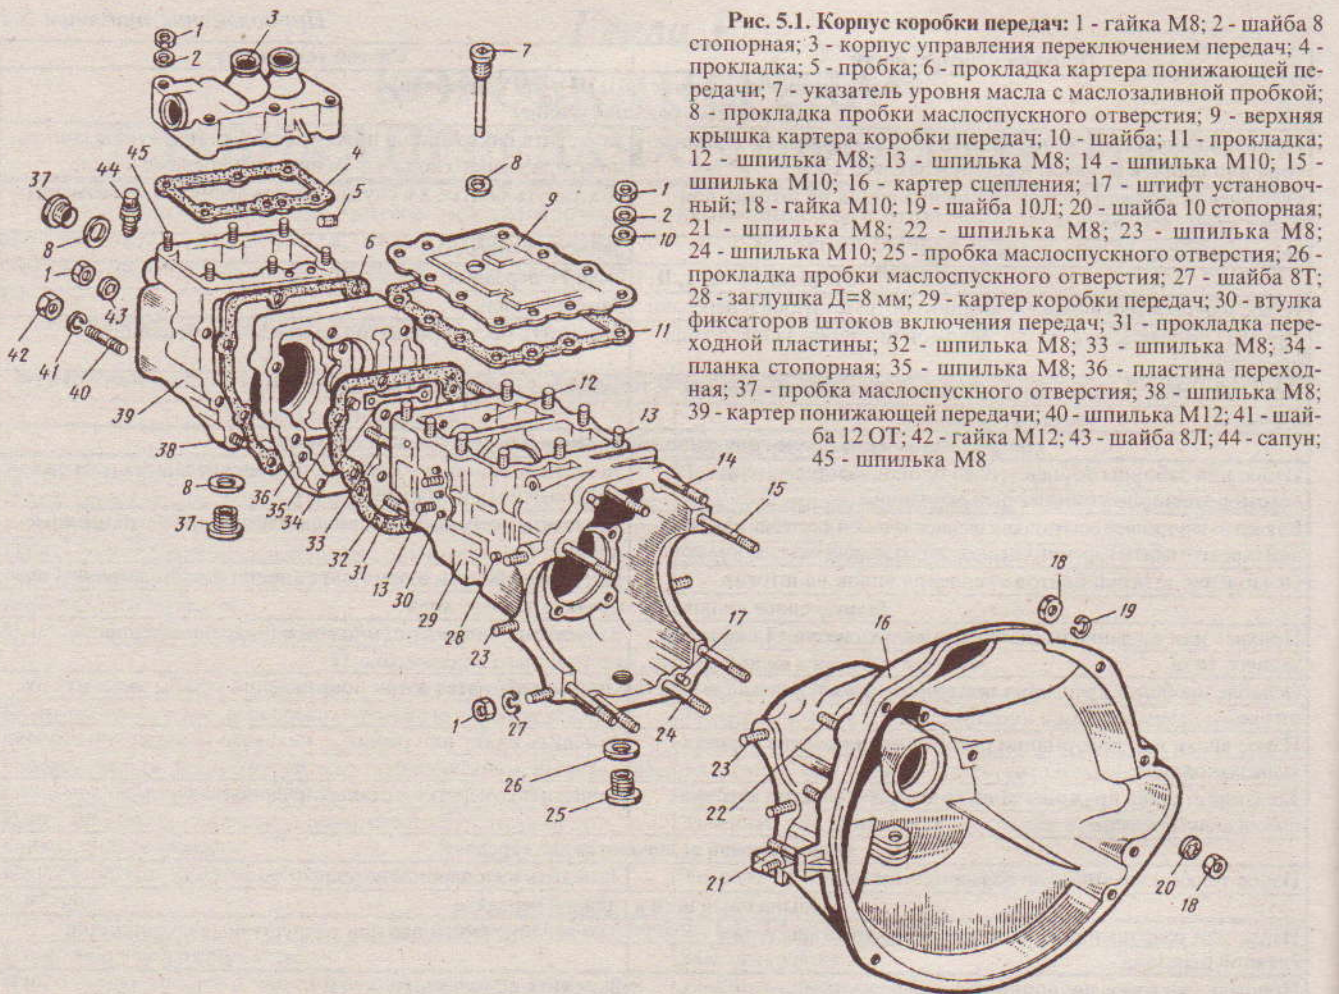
Корпус коробки передач: 1 - гайка М8; 2 - шайба 8 стопорная; 3 - корпус управления переключением передач; 4 - прокладка; 5 - пробка; 6 - прокладка картера понижающей передачи; 7 - указатель уровня масла с маслозаливной пробкой; 8 - прокладка пробки маслопускного отверстия; 9 - верхняя крышка картера коробки передач; 10 - шайба; 11 - прокладка; 12 - шпилька М8; 13 - шпилька М8; 14 - шпилька М10; 15 - шпилька М10; 16 - картер сцепления; 17 - штифт установочный; 18 - гайка М10; 19 - шайба 10Л; 20 - шайба 10 стопорная; 21 - шпилька М8; 22 - шпилька М8; 23 - шпилька М8; 24 - шпилька М10; 25 - пробка маслопускного отверстия; 26 - прокладка пробки маслопускного отверстия; 27 - шайба 8Т; 28 - заглушка $D=8$ мм; 29 - картер коробки передач; 30 - втулка фиксаторов штоков включения передач; 31 - прокладка переходной пластины; 32 - шпилька М8; 33 - шпилька М8; 34 - планка стопорная; 35 - шпилька М8; 36 - пластина переходная; 37 - пробка маслопускного отверстия; 38 - шпилька М8; 39 - картер понижающей передачи; 40 - шпилька М12; 41 - шайба 12 ОТ; 42 - гайка М12; 43 - шайба 8Л; 44 - сапун; 45 - шпилька М8
